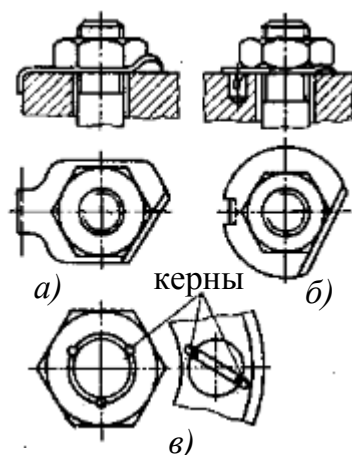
Стопорение резьбовых соединений деформируемой шайбой
